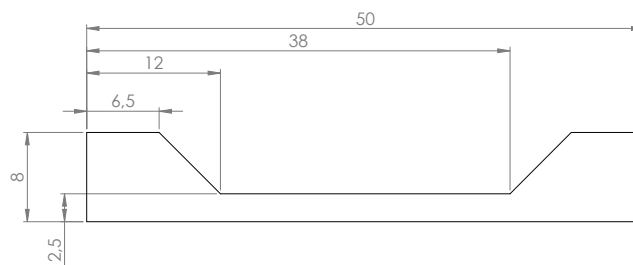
Mise en plan du substrat 3D V0 – vue de face
